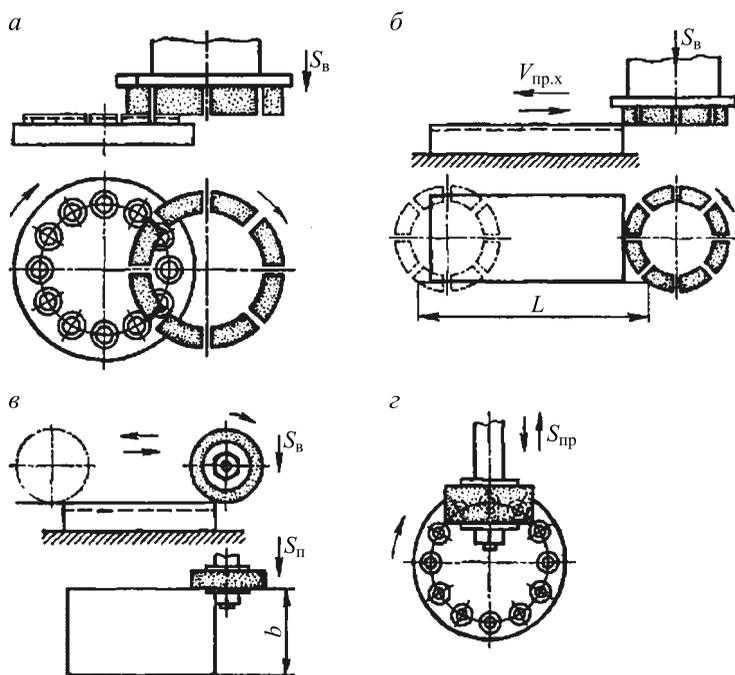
Схемы шлифования поверхностей: торцовым кругом: а — на круглом станке; б — на прямоугольном столе; цилиндрическим кругом: в — на круглом столе; г — на прямоугольном столе
